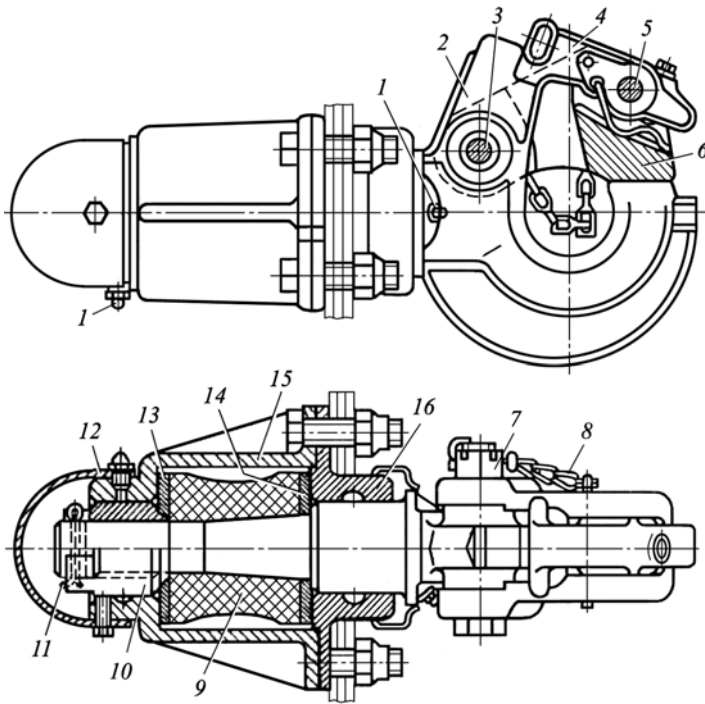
Тягово-зчіпний пристрій типу гак — петля:
